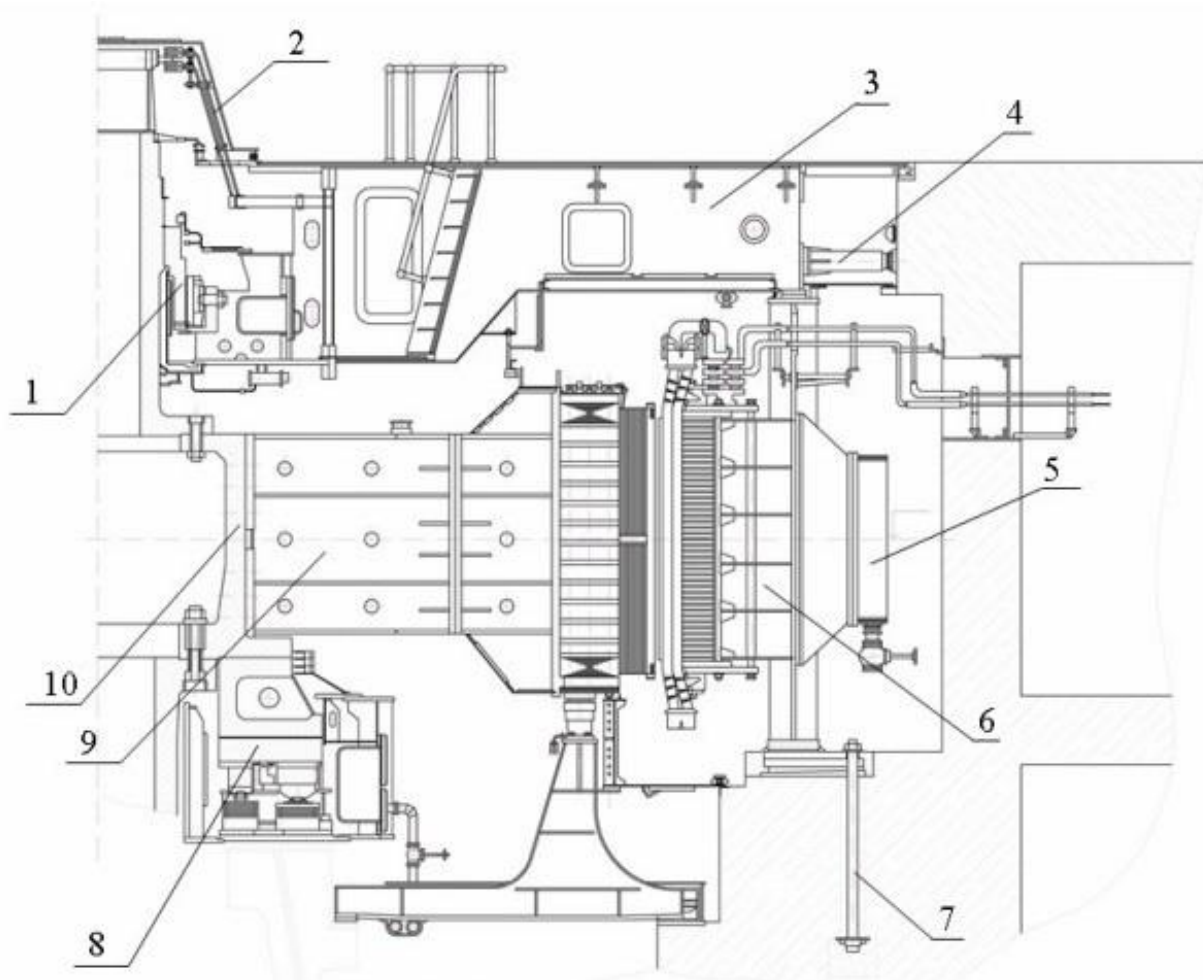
Загальна конструкція гідрогенератора-двигуна: 1 – напрямний підшипник; 2 – ковпак; 3 – хрестовина; 4 – розпирний домкрат; 5 – охолоджувачі повітря; 6 – статор; 7 – анкерні шпильки; 8 – упорний підшипник; 9 – ротор; 10 – втулка ротора
